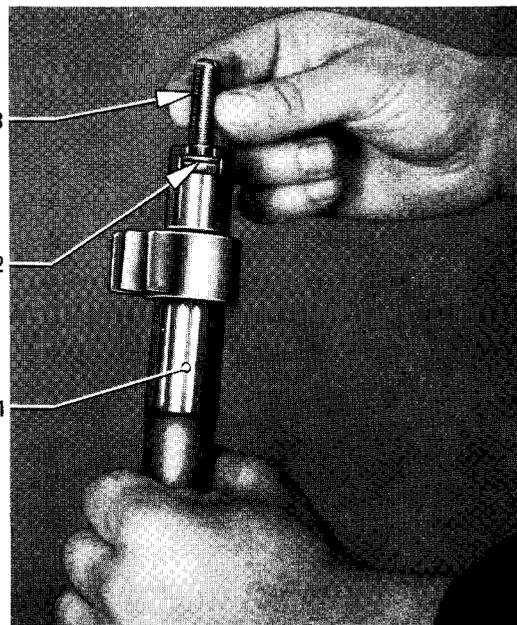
Einstellschraube mit Stahlscheibe in Lenkstockwelle einpassen
